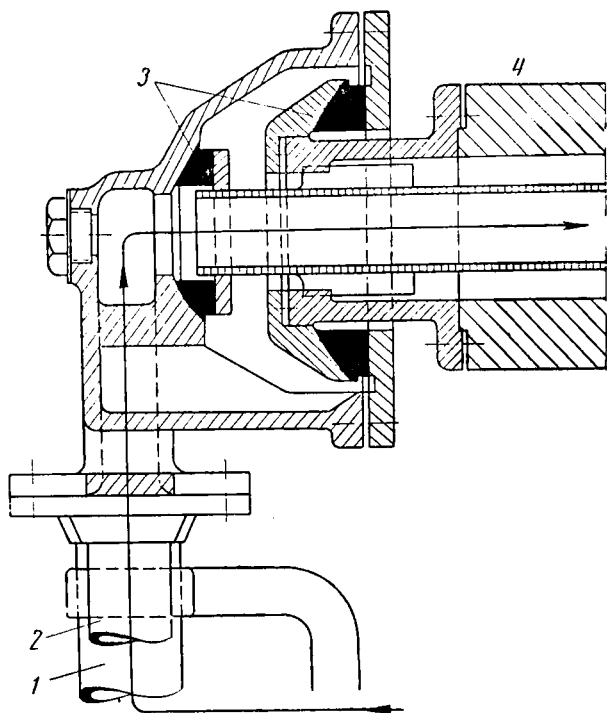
Паровпускная головка с графитными уплотнительными кольцами:
